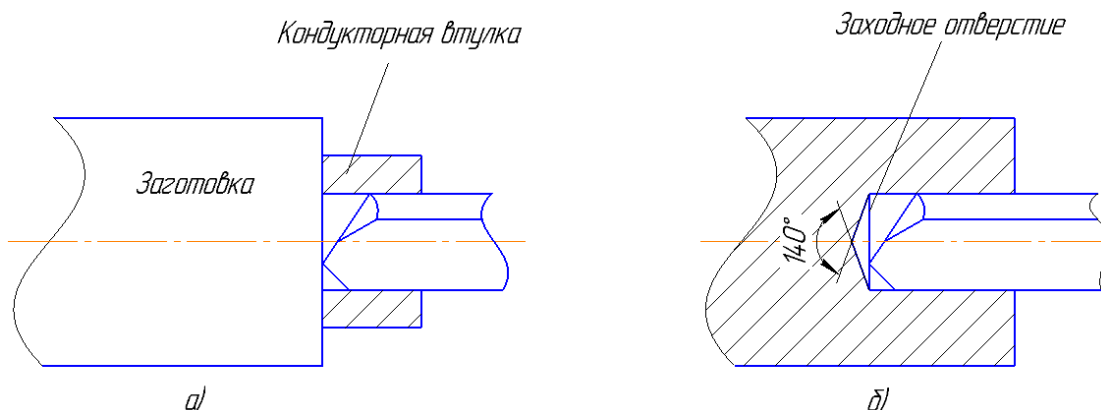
Способы врезания ружейных сверл: а) с помощью кондукторной втулки;
